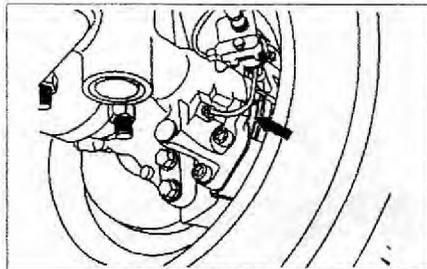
Проверьте толщину внутренней прокладки тормозной колодки дискового тормозного механизма заднего колеса через отверстие (стрелка).
